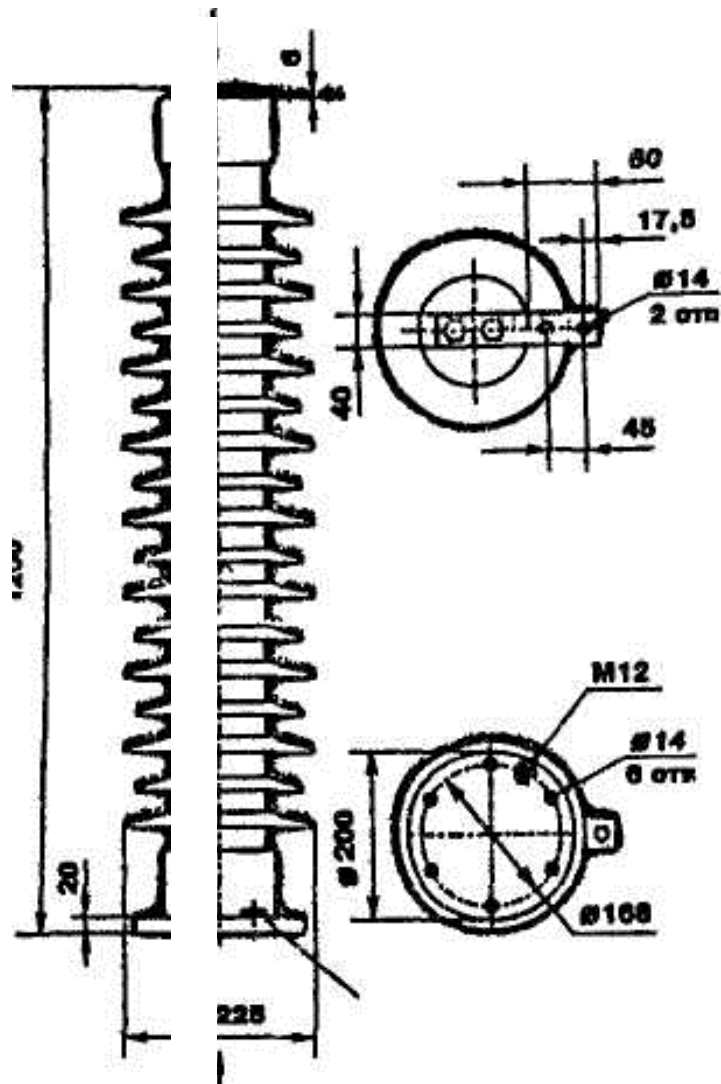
Общий вид и основные размеры ОПН-У/ТЕЛ-110
